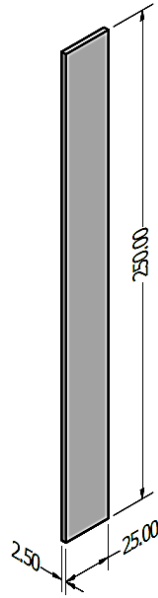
Dimensiones de las probetas de ensayo en mm
